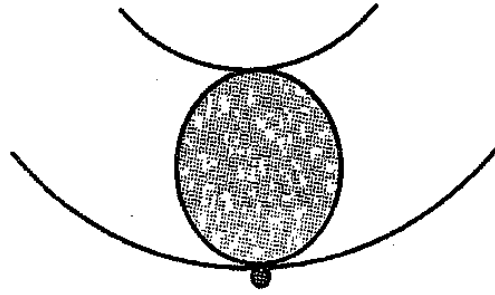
Paso de un elemento rodante sobre un defecto en pista externa
